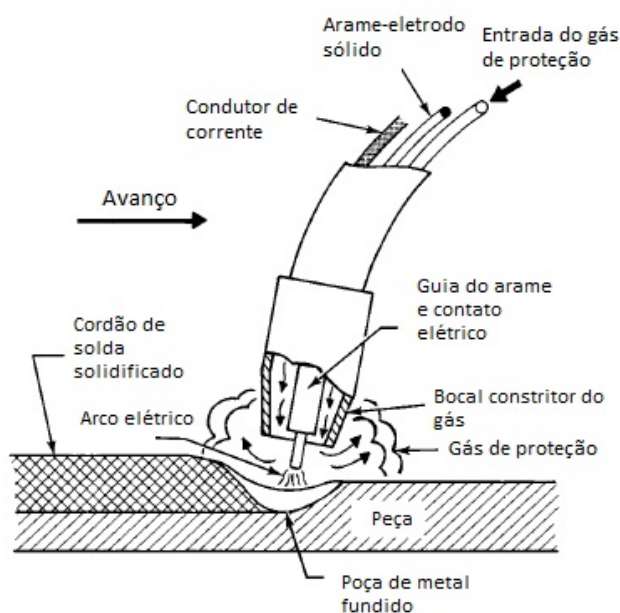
Representação de tocha MIG/MAG e seus elementos durante a soldagem.
